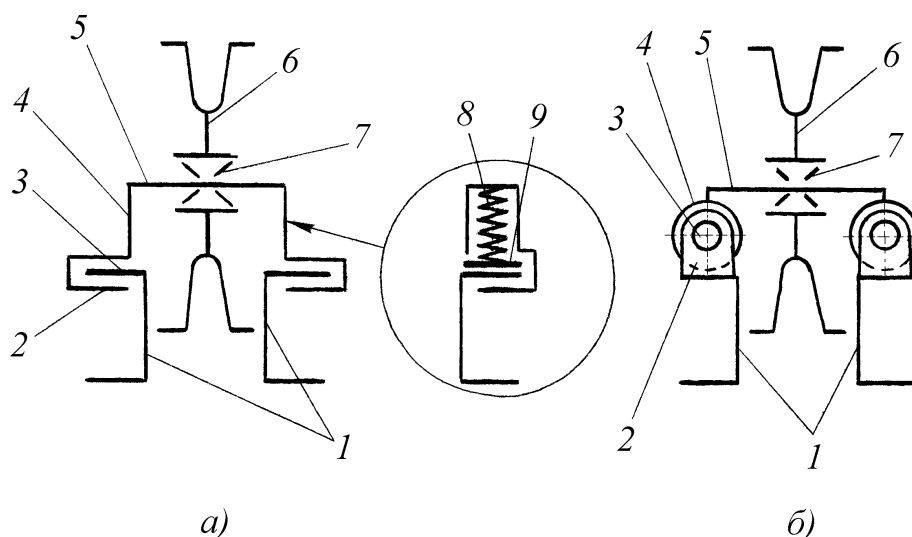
Схемы установки направляющего колеса на ползунах
